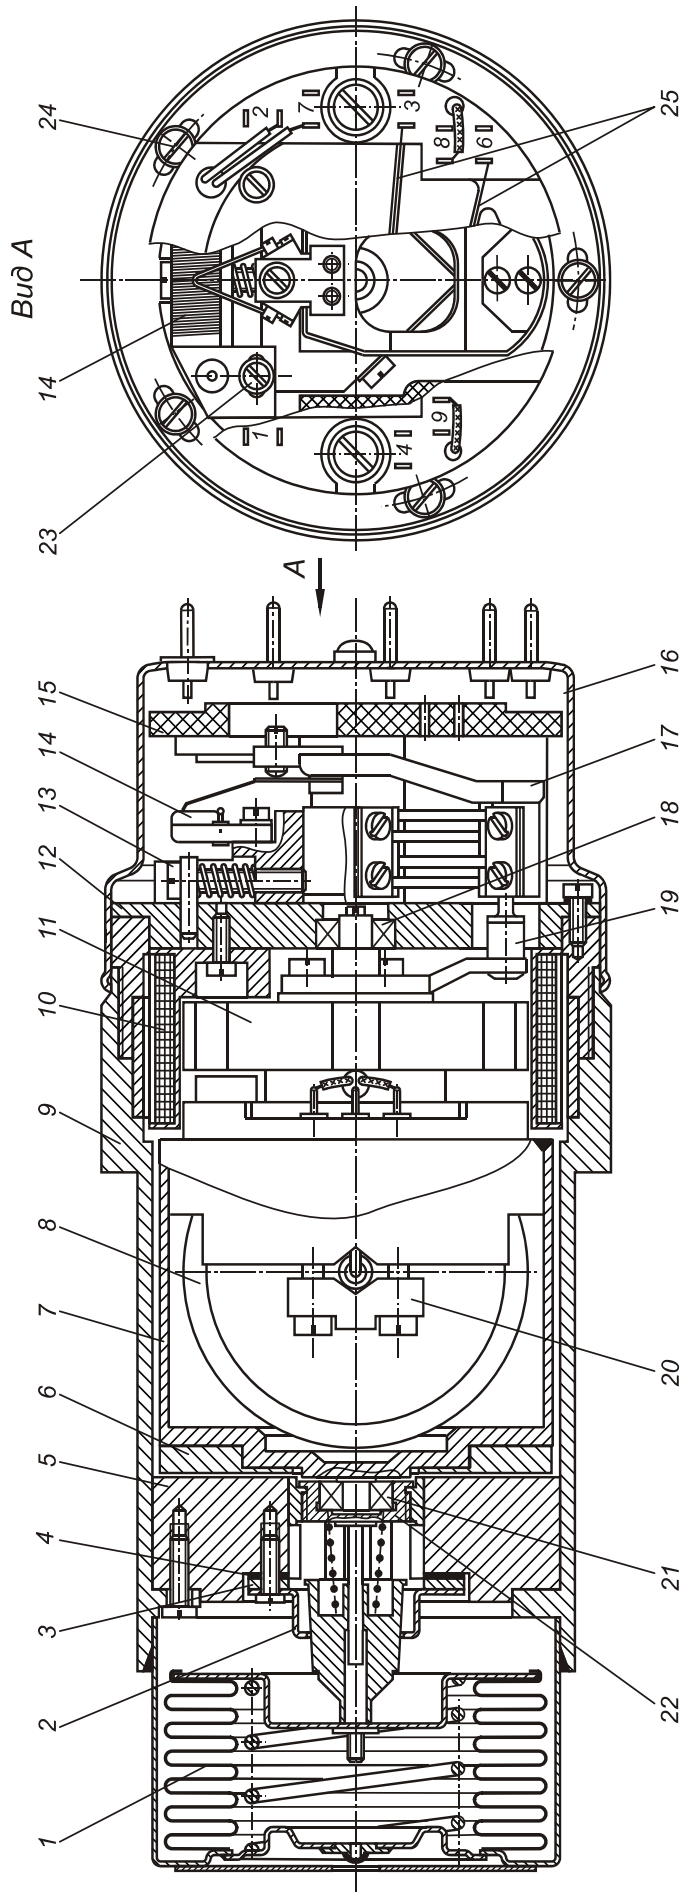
Гіроскопічний тахометр ДУСУ: 1 – вузол сільфону; 2 – діафрагма; 3 – втулка; 4 – прокладка; 5 – статор; 6 – ротор; 7 – гіровузол; 8 – гіромотор; 9 – корпус; 10 – вузол когушок; 11 – магніт; 12 – фланець; 13 – гвинт регулювальний; 14 – потенціометр; 15 – колодка; 16 – вузол кришки; 17 – передатний механізм; 18 – підшипник; 19 – палець; 20 – планка; 21 – підшипник; 22 – втулка; 23 – гвинт регулювальний; 24 – гвинт; 25 – струмовідвід.
